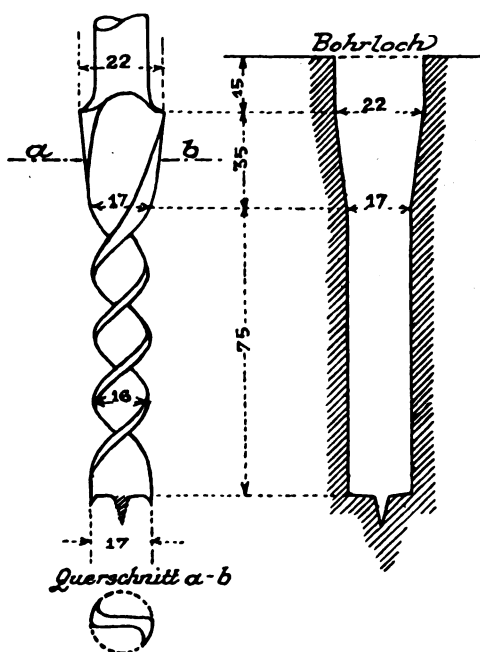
Bohrer für verstärkte Schwellenschrauben Form A.
